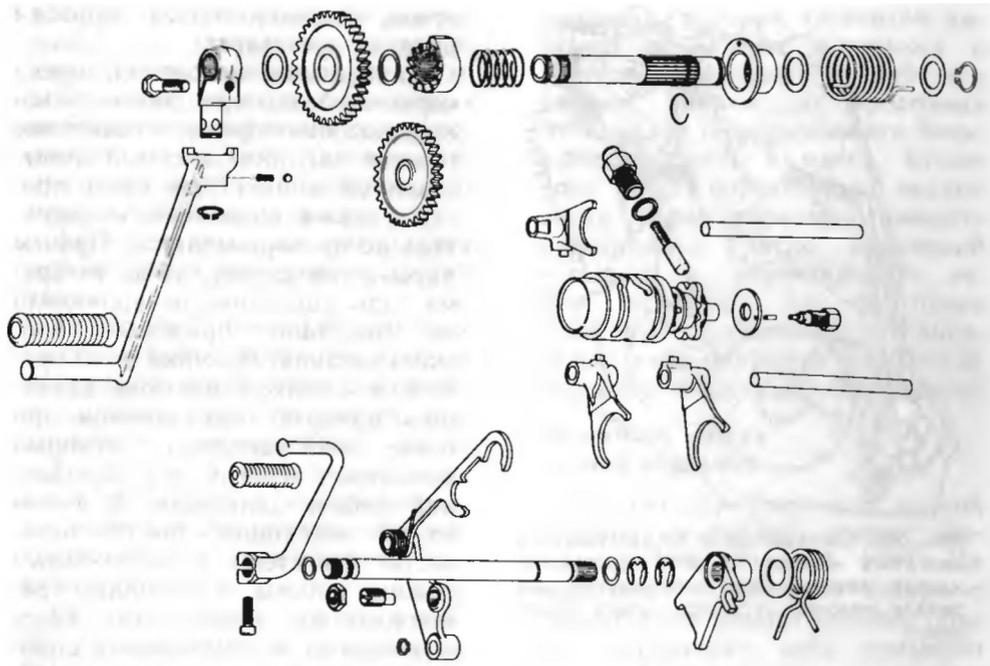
Пример комбинации переключающего механизма с устройством пуска двигателя
